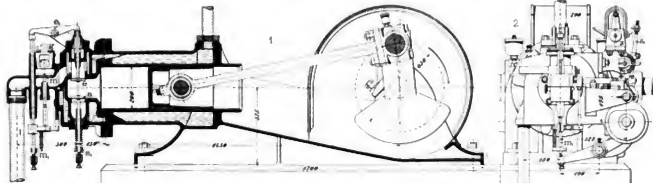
Z. A.: Die Hornsby-Stockport-Gasmaschine.
